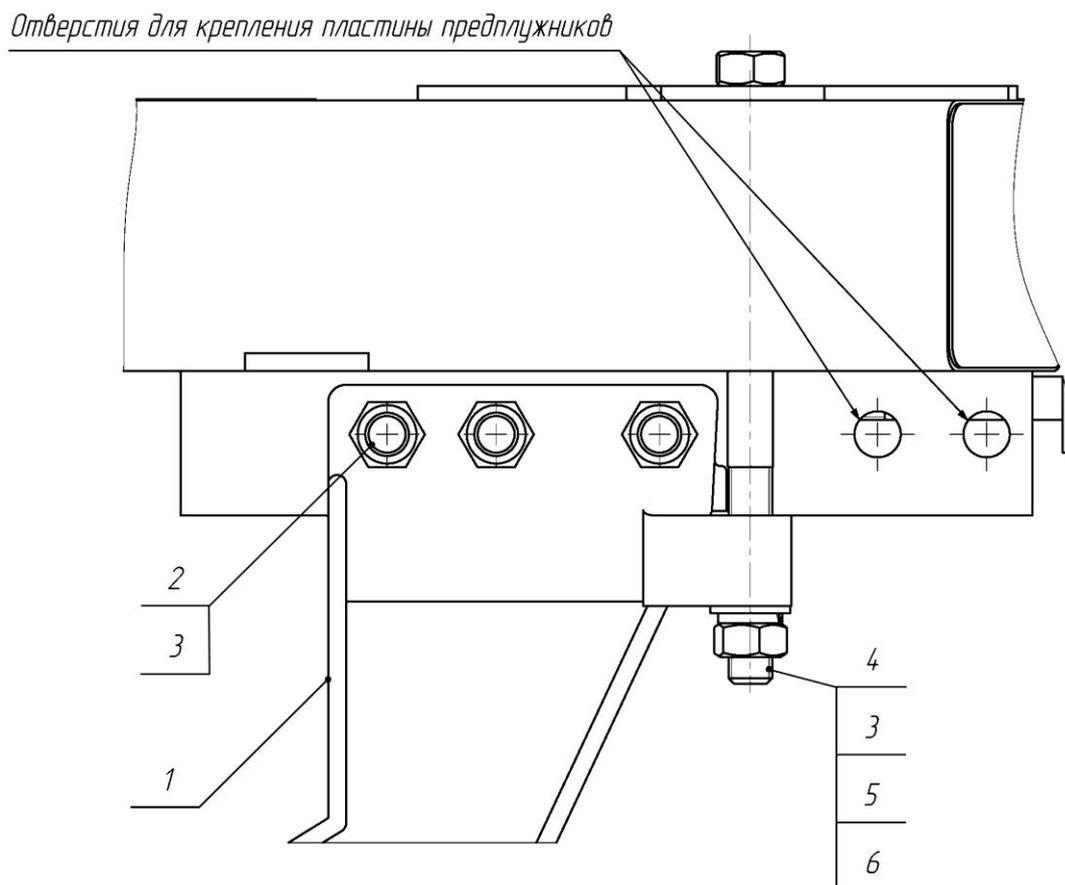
а Установка колеса на ПЛУ-5-35/ПЛУ-5-35П
